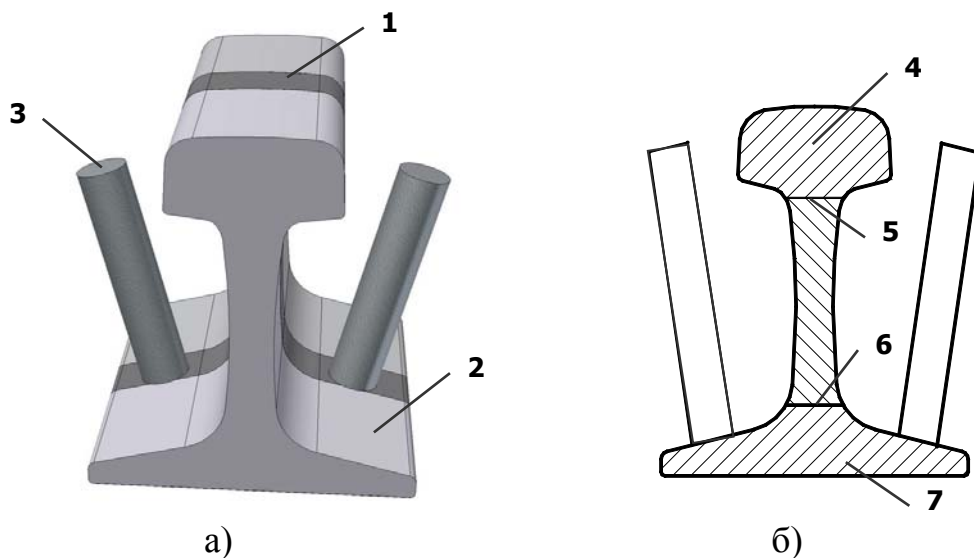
Алюминотермитное сварное соединение рельса: а) общий вид, б) схема, 1-сварной шов, 2 - рельс, 3 – литник, 4 - головка рельса, 5 - верхняя часть шейки рельса, 6 - нижняя часть шейки рельса, 7 - подошва рельса.
